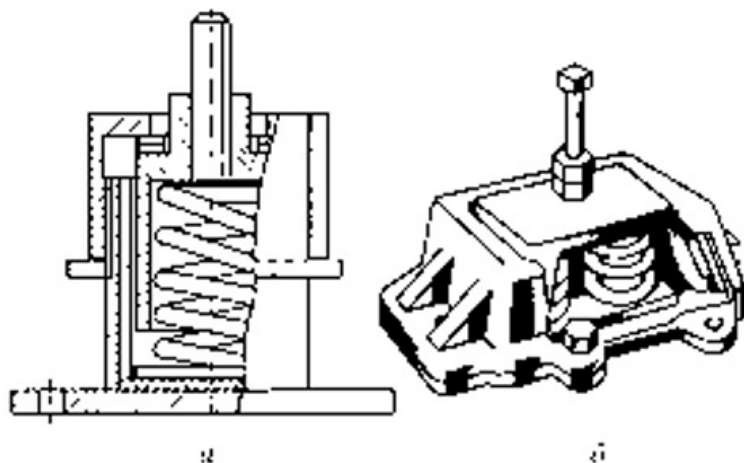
Пружинный и комбинированный виброизоляторы: а — цилиндрический пружинный амортизатор; б — пружинно-резиновый амортизатор
